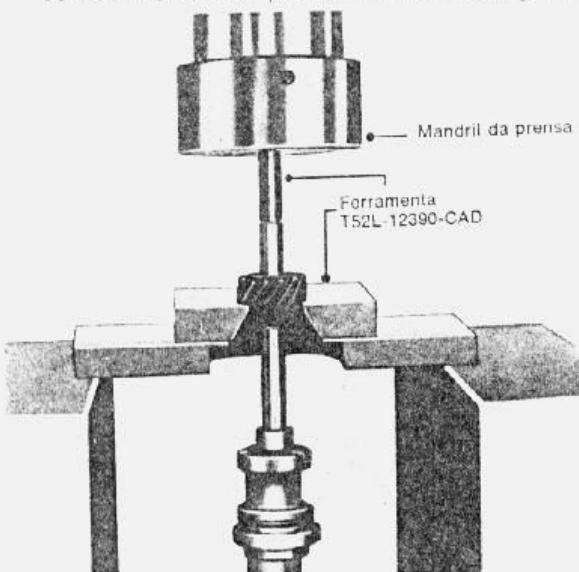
remoção da engrenagem da árvore do distribuidor - motor de 8 cilindros
